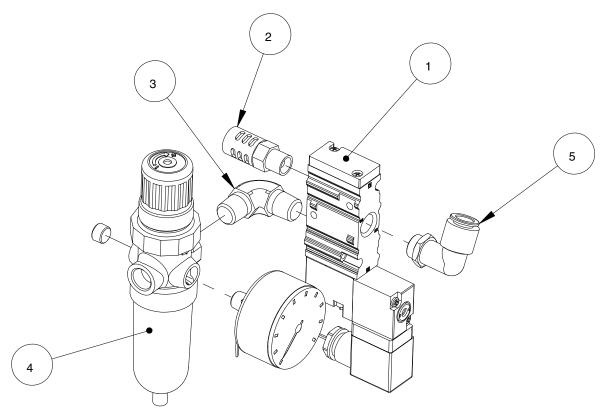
Ersatzteile Baugruppe Regler/Magnetventil
